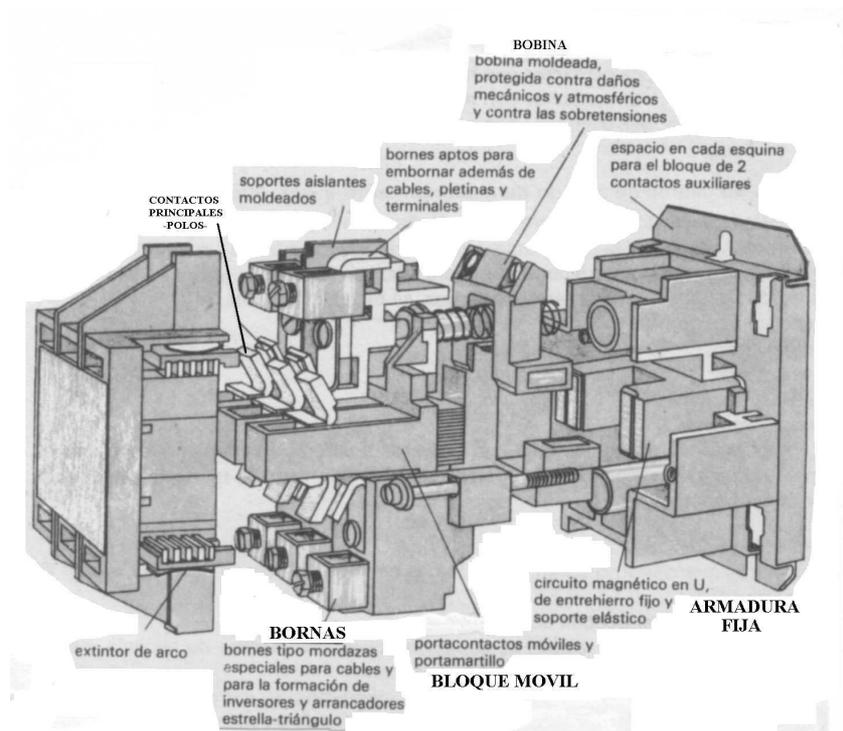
CONSTITUCIÓN DE UN CONTACTOR
